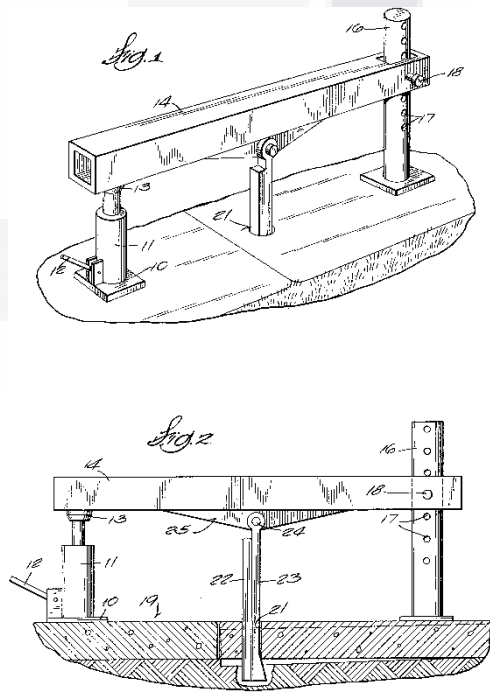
Device for hydraulic lift of reinforced concrete (Laurance Kaderabek, 1981)
